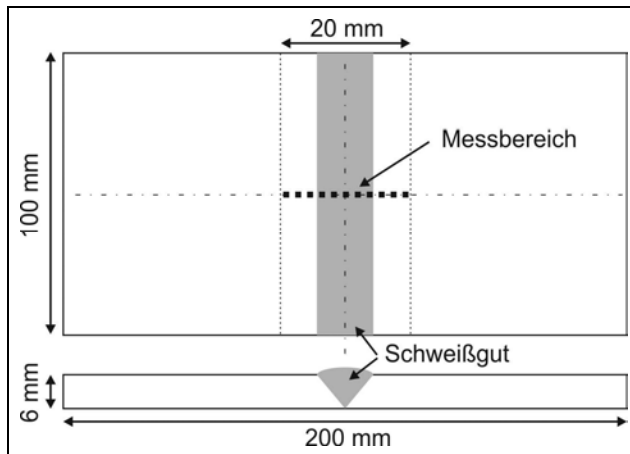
Probenform und Eigenspannungsmessbereich für zweilagige Schweißnähte am hochfesten Feinkornstahl S690QL mit einer Plattendicke von 6 mm
